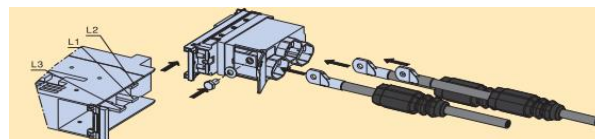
/ Fig. 22: assembly SASILplus double pluggable
